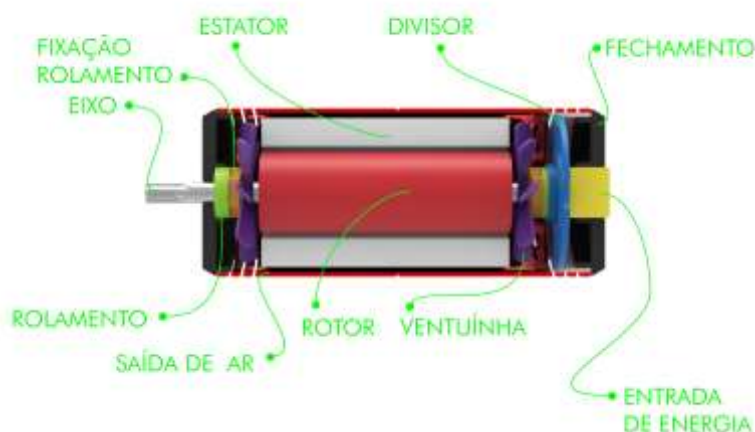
Esquema de estrutura do motor. Fonte: Autor.
